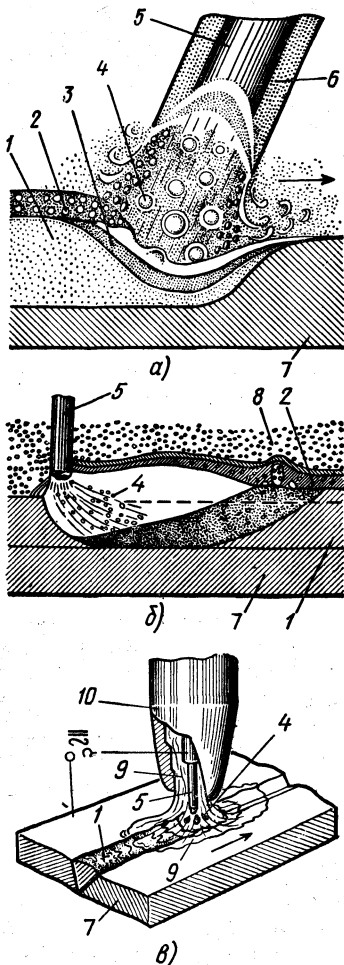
Виды дуговой сварки: а — электродом с покрытием, б — под флюсом, в — в углекислом газе; 1 — шов, 2 — шлак, 3 — сварочная ванна, 4 — капли металла, 5 — электрод, 6 — защитное покрытие, 7 — основной металл, 8 — флюс, 9 — защитный газ, 10 — сопло
